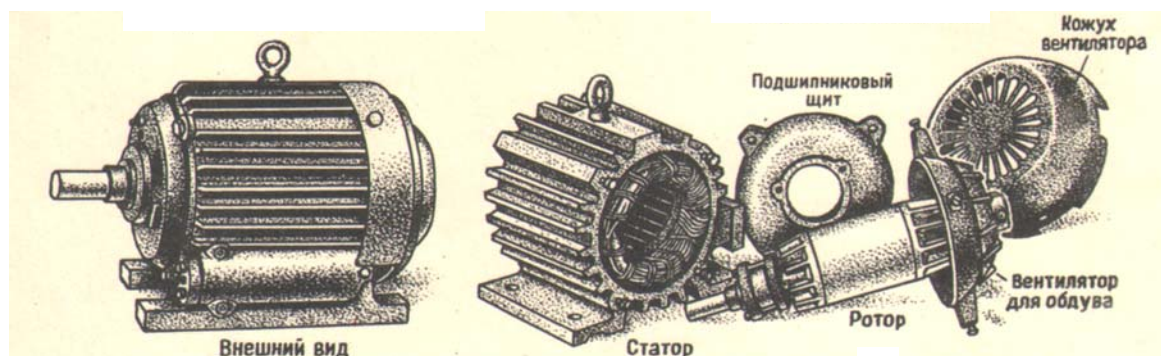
Асинхронный электродвигатель серии АО, внешний вид (слева) и элементы его конструкции (справа).
